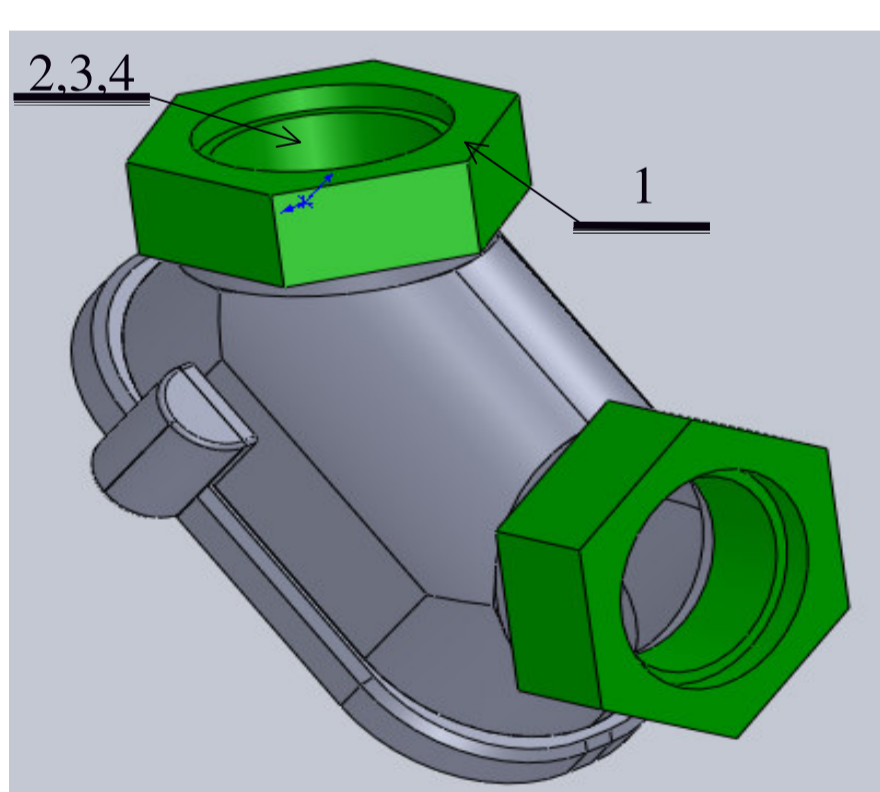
Model odlew części klasy odlew z wyznaczeniem zabiegów do pierwszej operacji i wraz z koncepcją zamocowaniem
